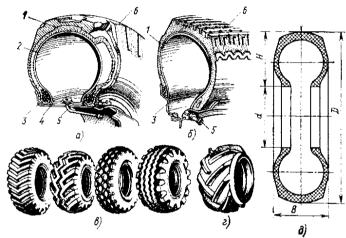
Пневматические шины: а – камерная; б – бескамерная; в – типы рисунков протекторов; г – арочная; д – основные размеры шины; 1 – покрышка; 2 – камера; 3 – обод колеса; 4 – ободная лента (флеп); 5 – вентиль; 6 – протектор
